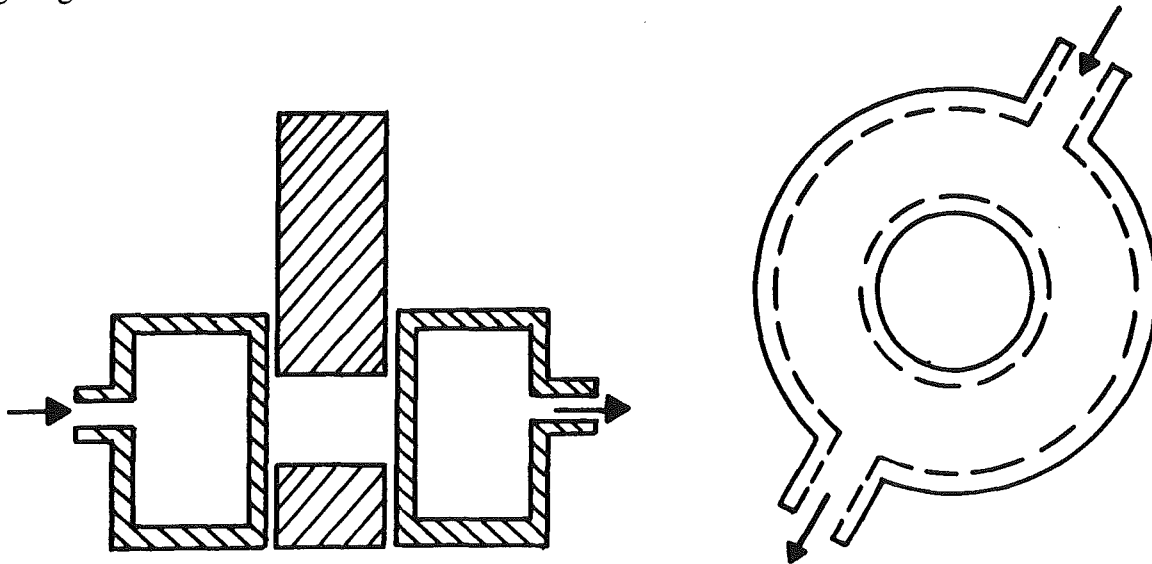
Zylindrisch ausgedrehter Cu-Block mit Wasserkühlung; Seitenansicht, Aufsicht.
